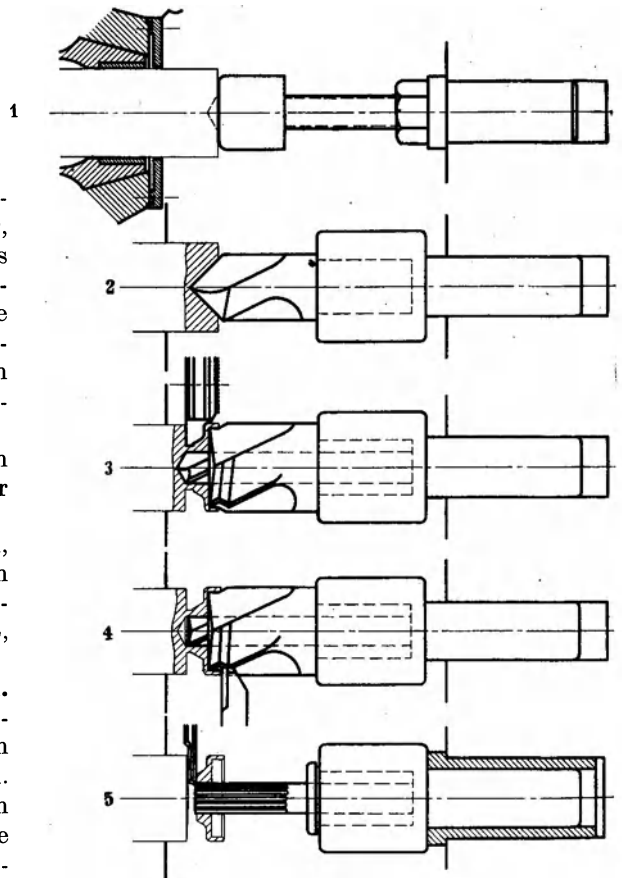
Bearbeitung einer Kappe aus Stahl.
